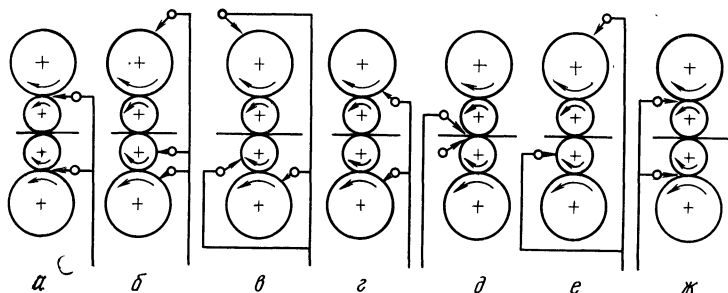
Схемы подачи технологической смазки на валки [282]:
